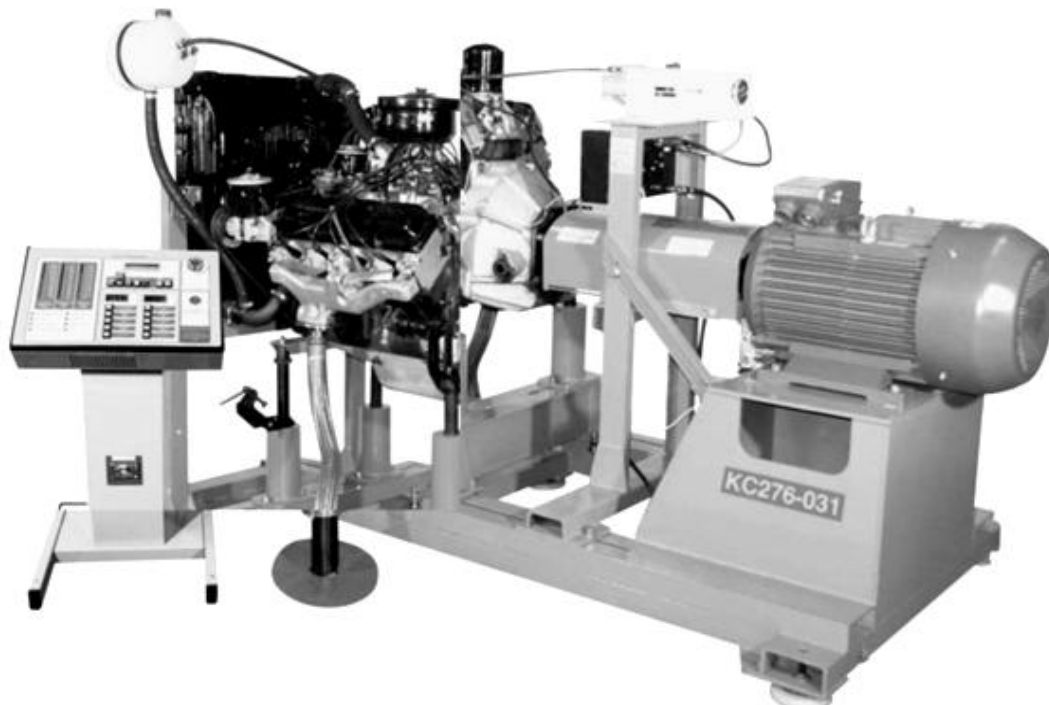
Стенд для обкатки двигателей КС-276-031
